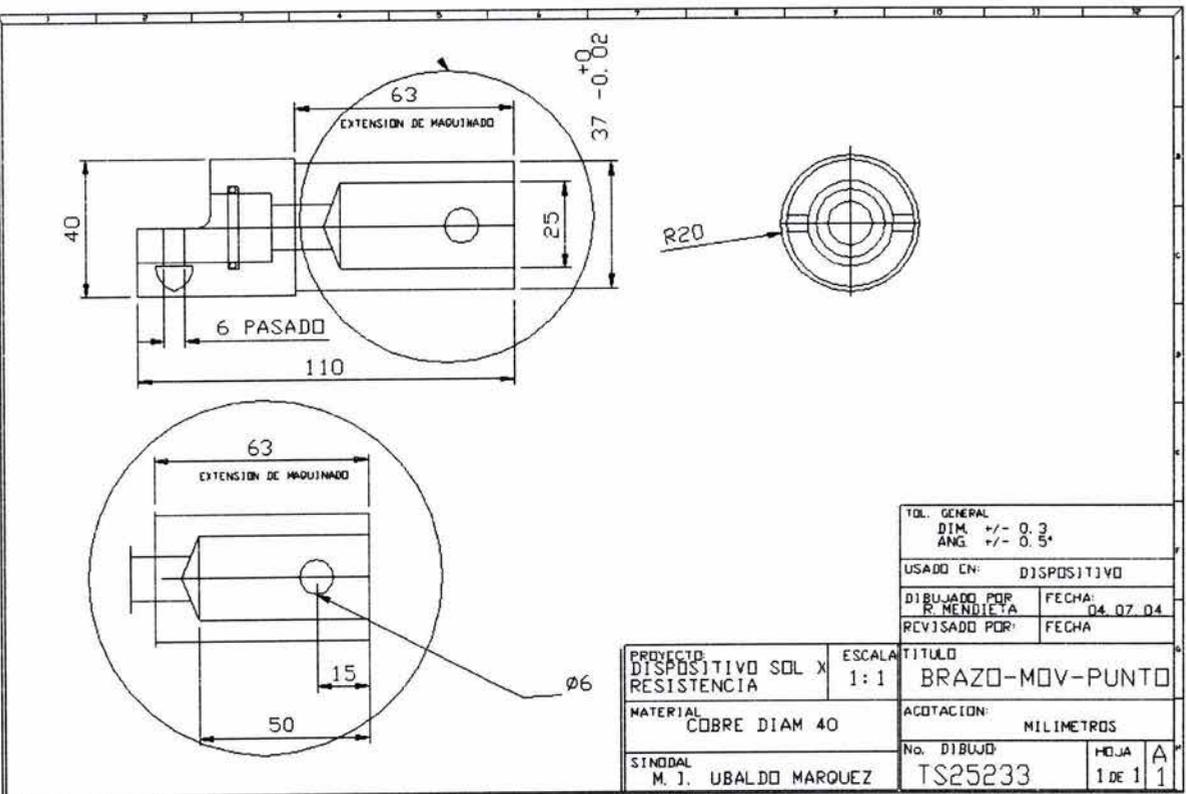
Brazo móvil para soldadura por resistencia de punto.
